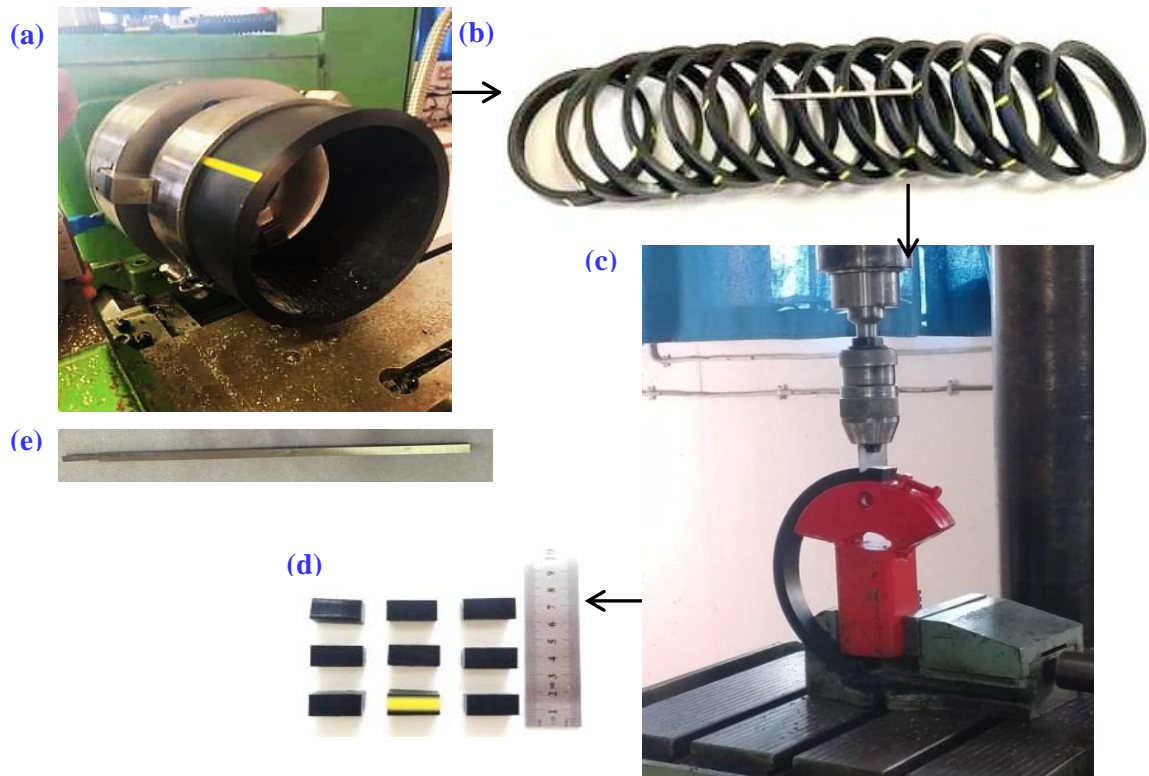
Usinage des parallélépipèdes. a) Pipe HDPE sur tour universel b) Anneaux c) Découpe des éprouvettes d) Eprouvettes. e) Outil de rainurage
